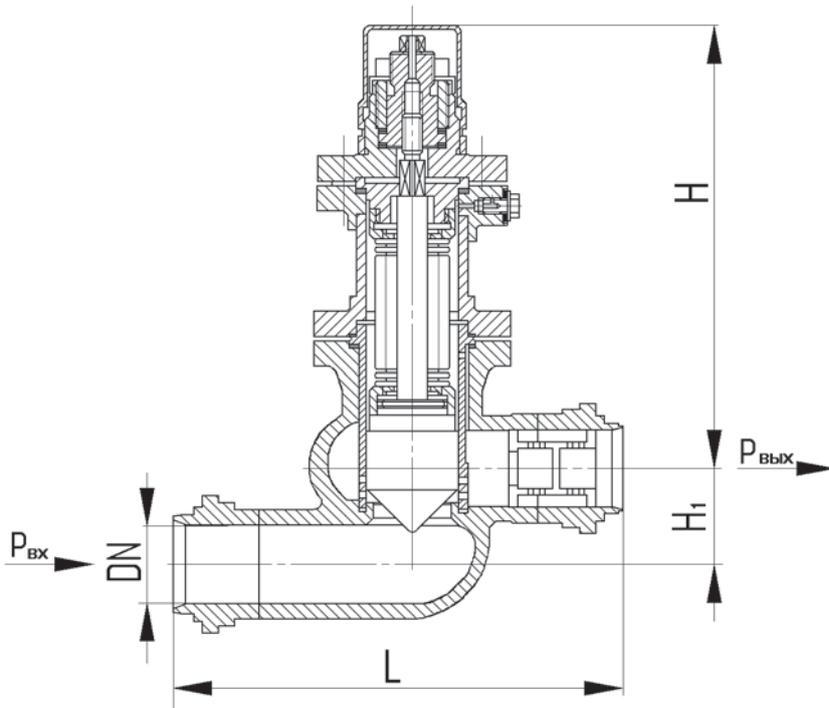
Клапан дроссельный проходной с патрубками под приварку
